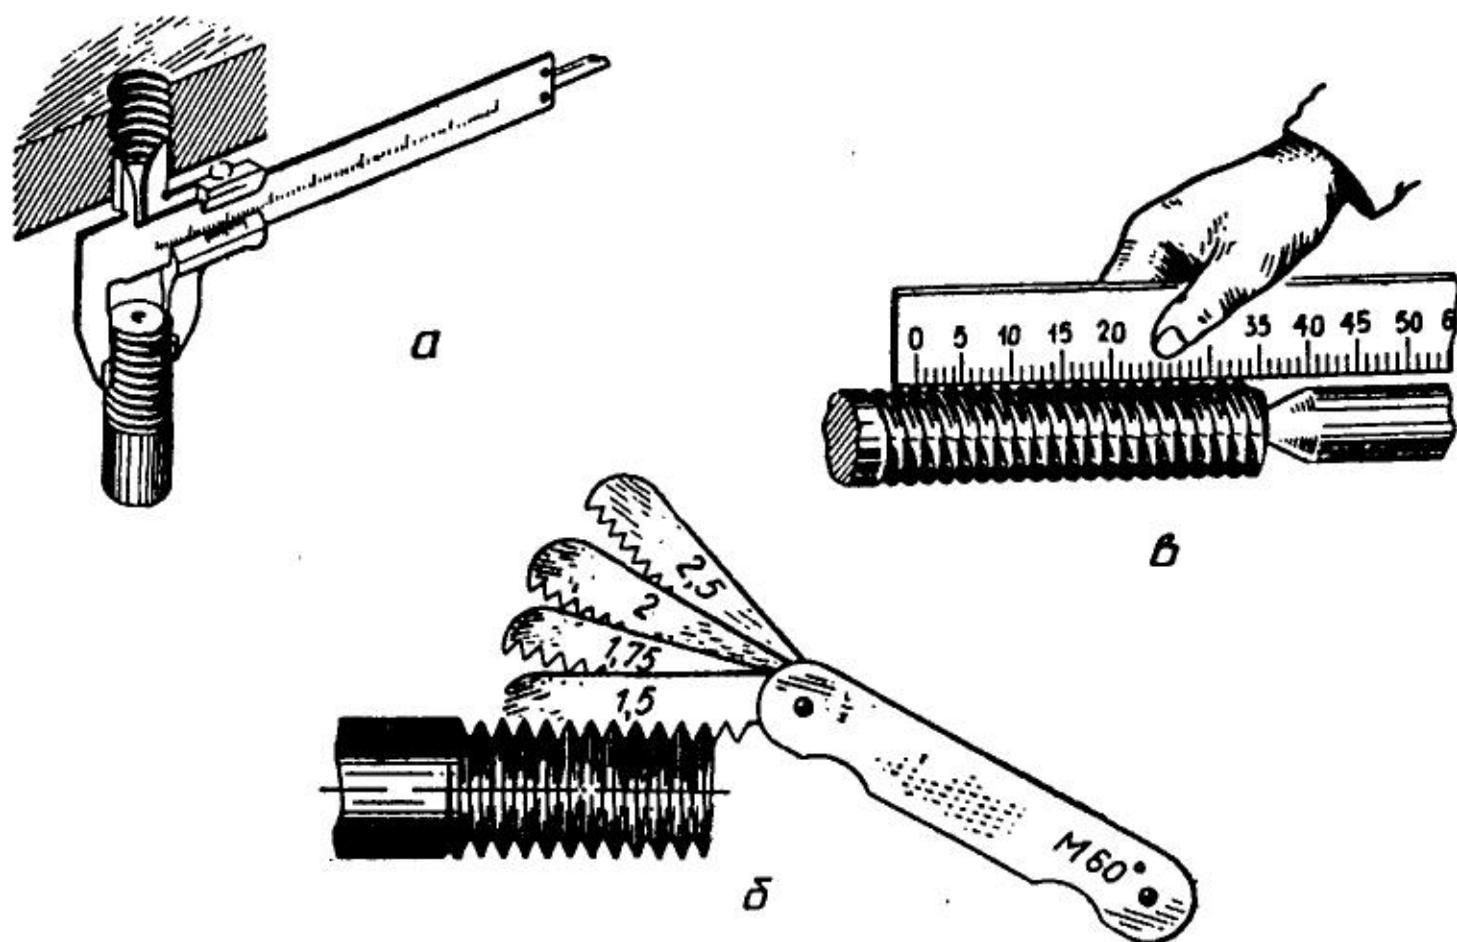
Вимірювання розмірів різьби: зовнішнього діаметра (а) — штангенциркулем; кроку різьби — різьбоміром (б) і лінійкою (в) — за виступами вершин ниток різьби.
